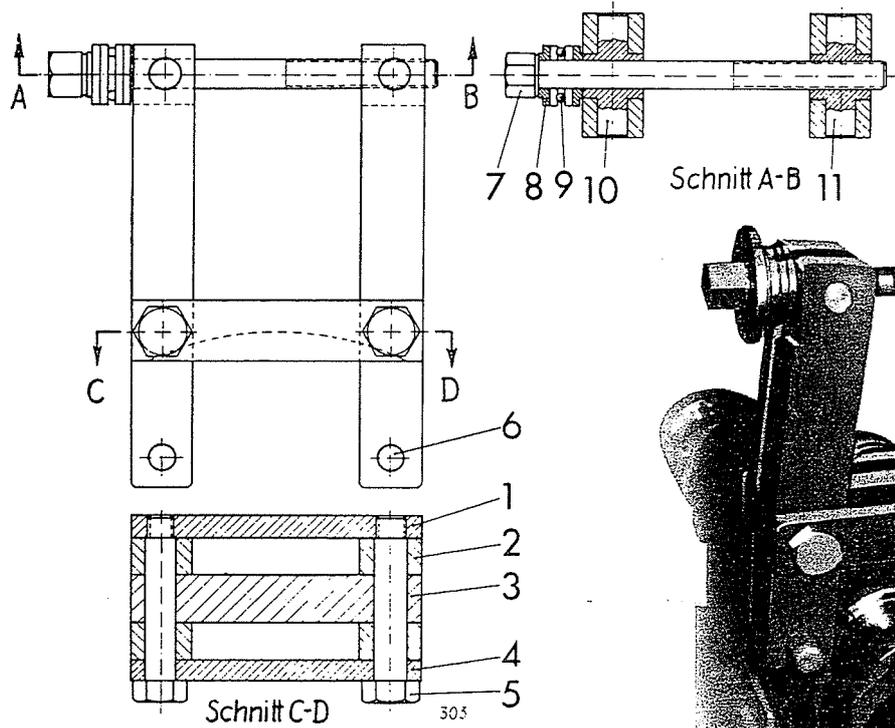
Spannvorrichtung für Gegengewichte der Kurbelwellen
